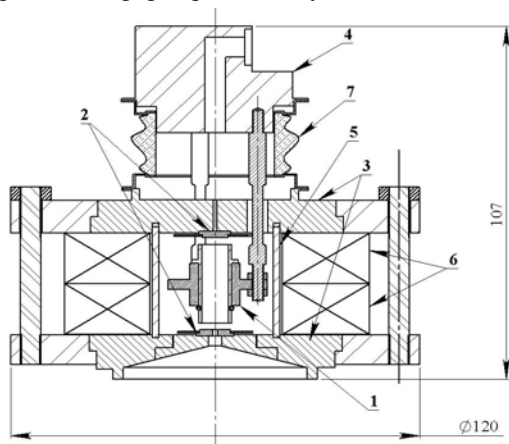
а. Схема ИМИ: 1 - полый цилиндрический анод; 2 – катоды; 3 – катодные фланцы (магнитопровод); 4 - анодный фланец; 5 – корпус; 6 - постоянные магниты; 7 - керамический изолятор
